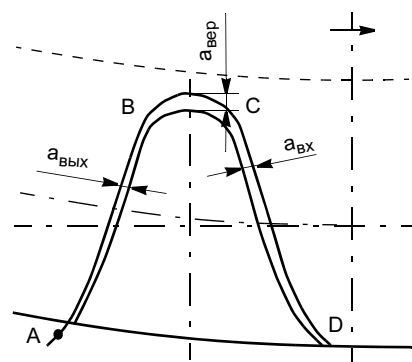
Форма срезаемых слоев червячной фрезой для колес зацепления Новикова
